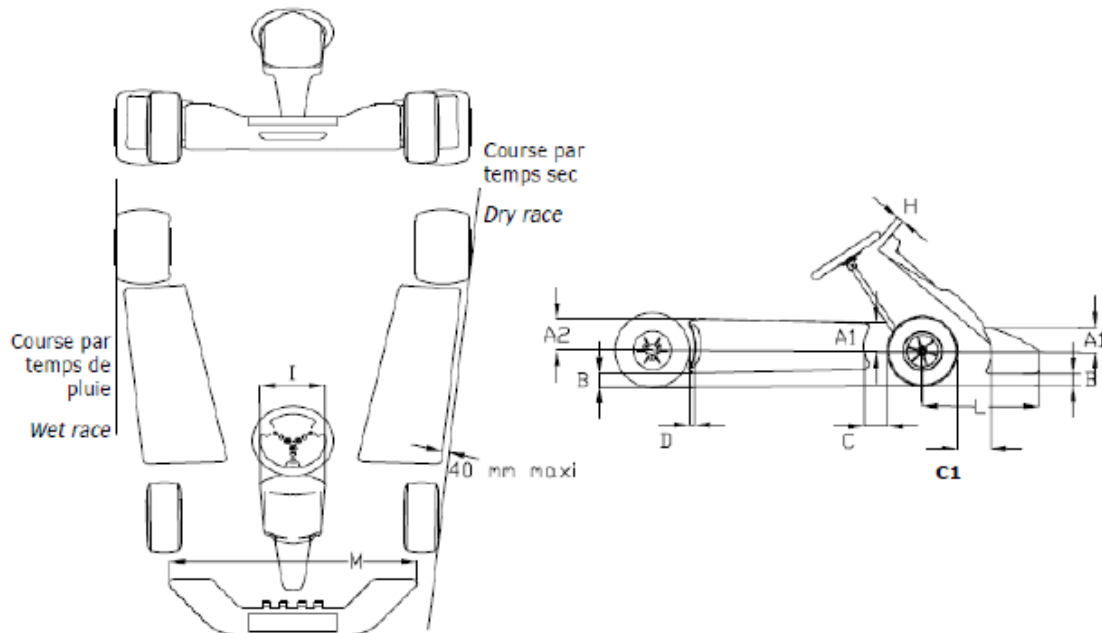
dimensiones del carenado. Fuente: CEK 2019 DIBUJOS TÉCNICOS
